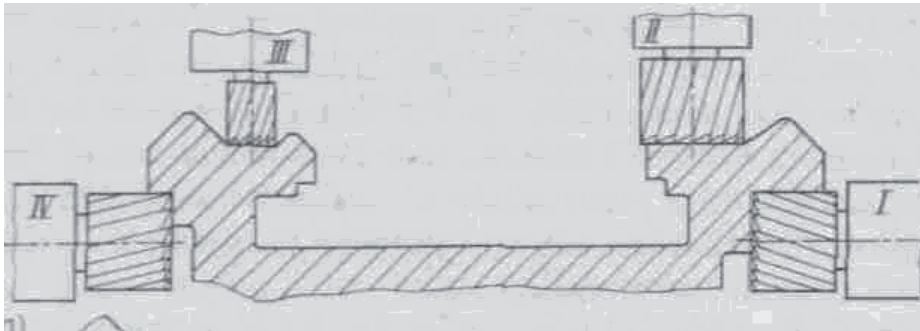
Схема одновременной обработки шести поверхностей станины токарного станка на четырехшпиндельном продольно-фрезерном станке
